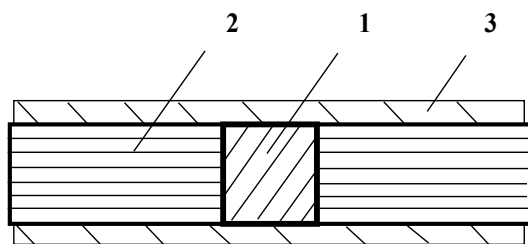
Схема установки образца для прокатки 1-образец; 2-стальная пластина; 3-чехол из меди
